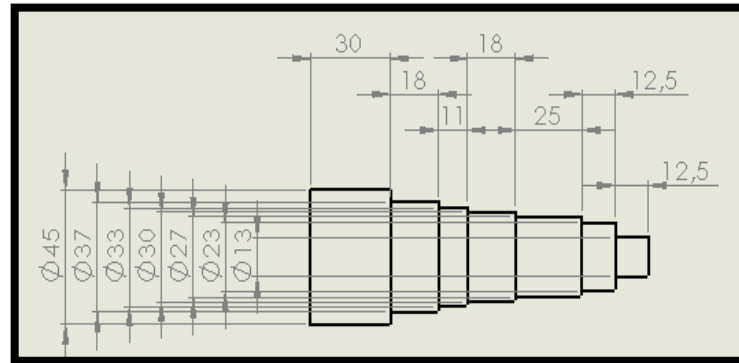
Dimensiones de pieza de pruebas de penetración.
